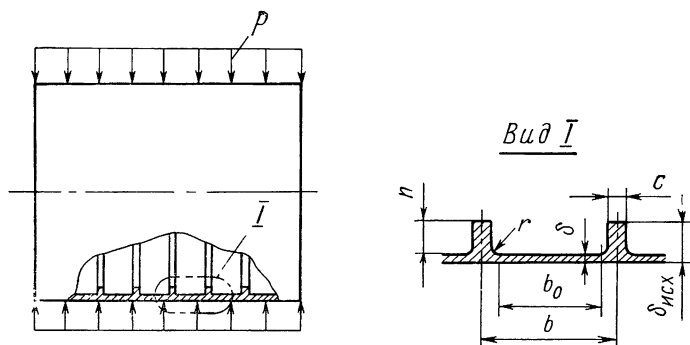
Цилиндрическая оболочка с кольцевыми ребрами, нагруженная внешним давлением
